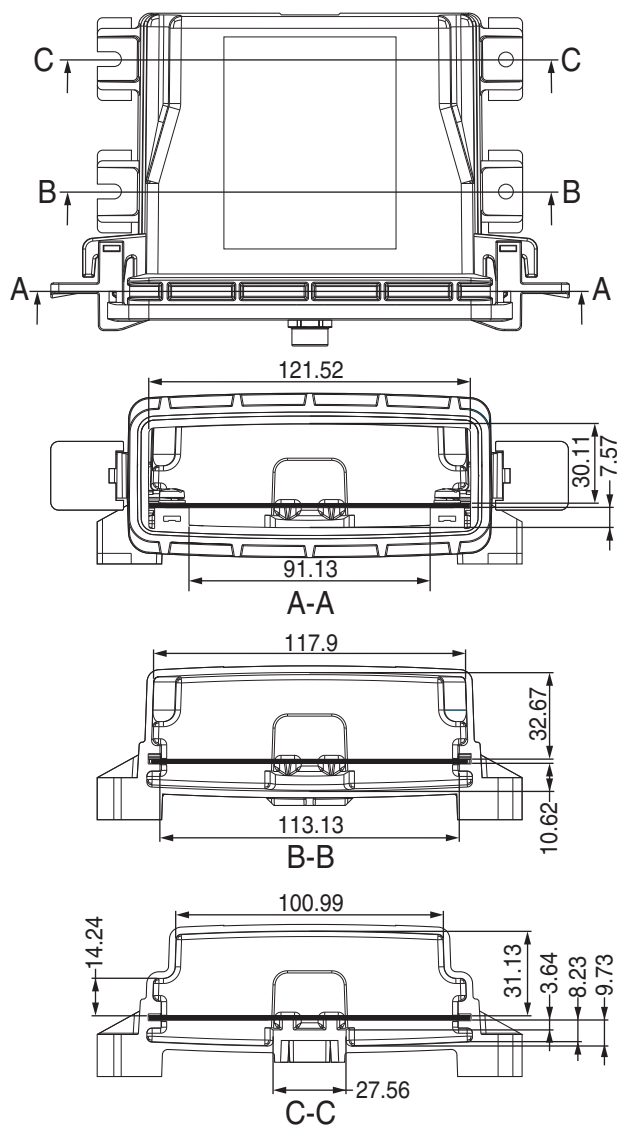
Innenansicht Gehäuse mit Leiterplatte
